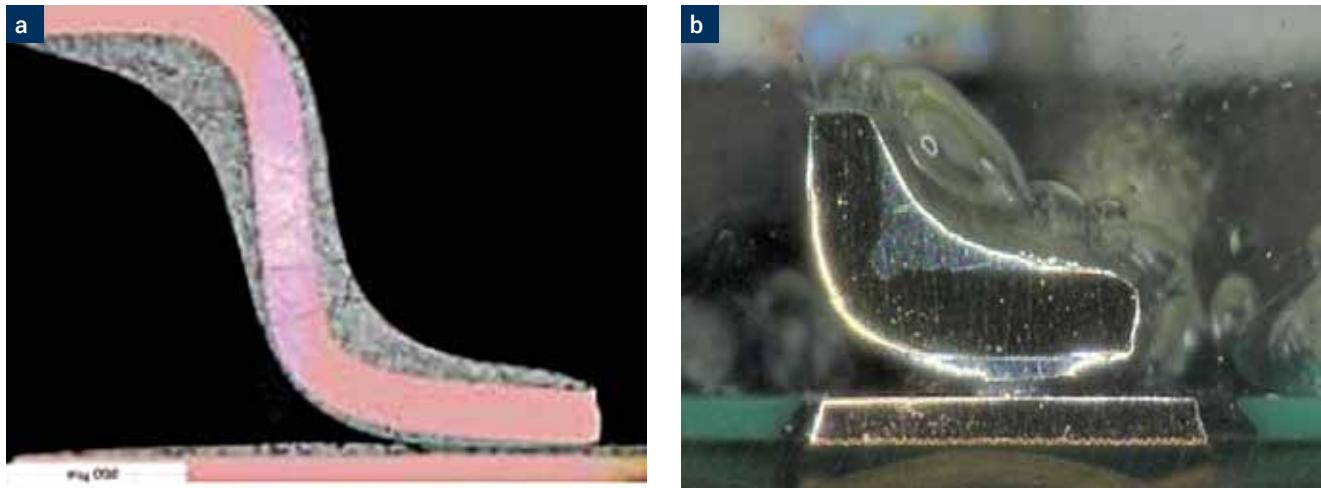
Beispiele für Wicking an einem Gullwing (a) und an einem Steckverbinder-Kontakt (b)
